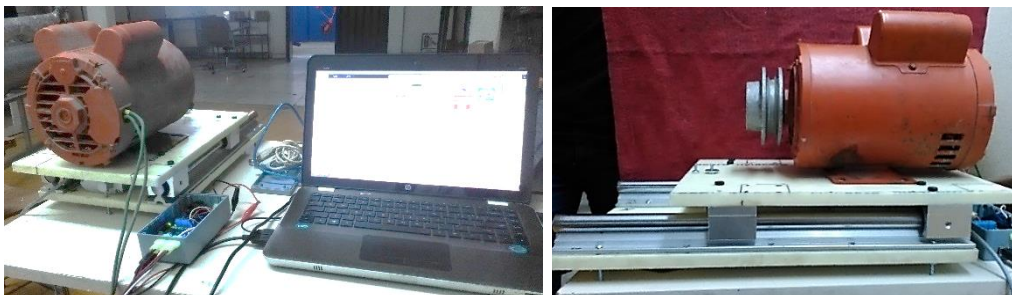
Mecanismo de ajuste con el motor de disco de corte montado.
